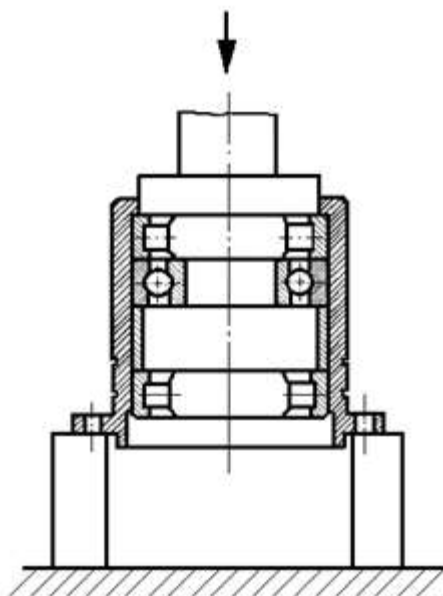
Разборка деталей подшипников, втулки.
